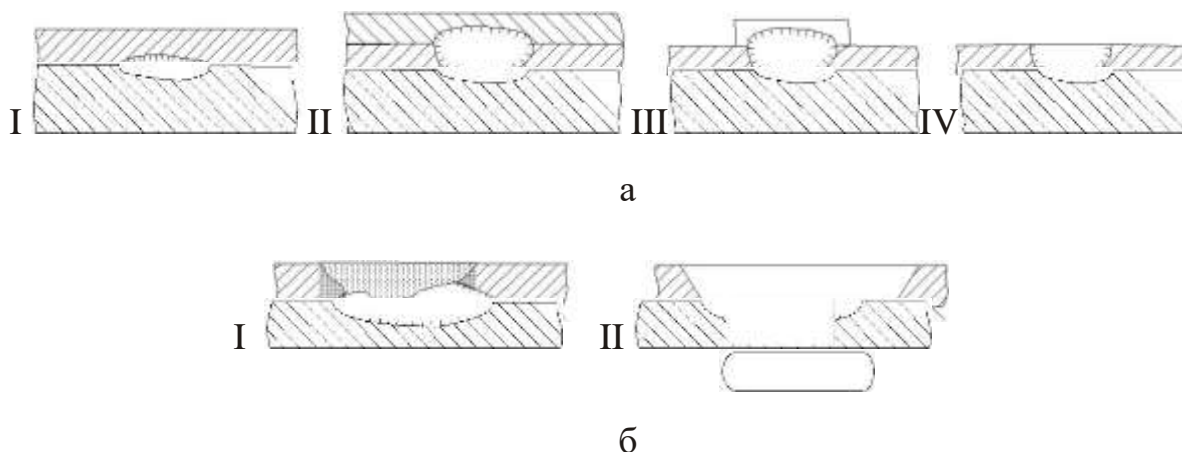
Исправление дефектов точечной сварки:
